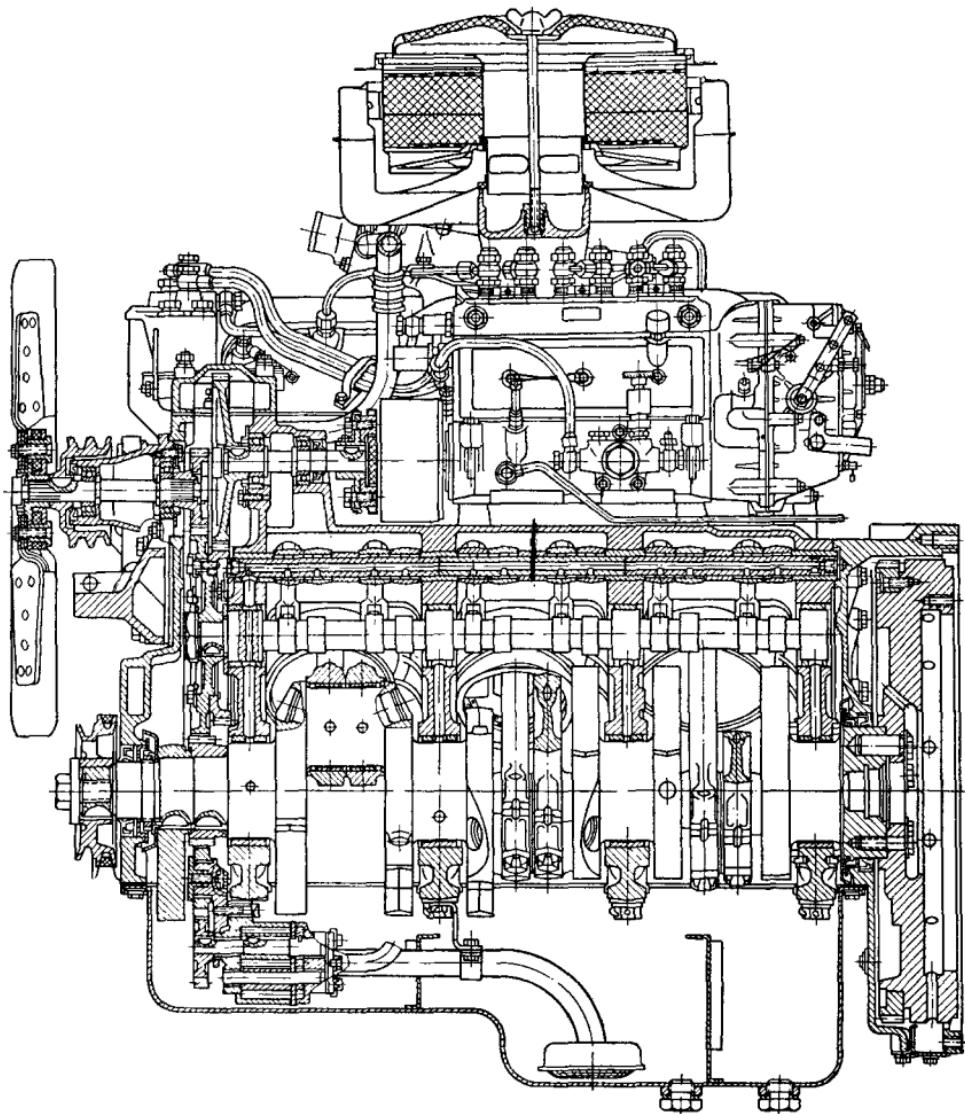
Продольный разрез двигателя ЯМЗ-236
